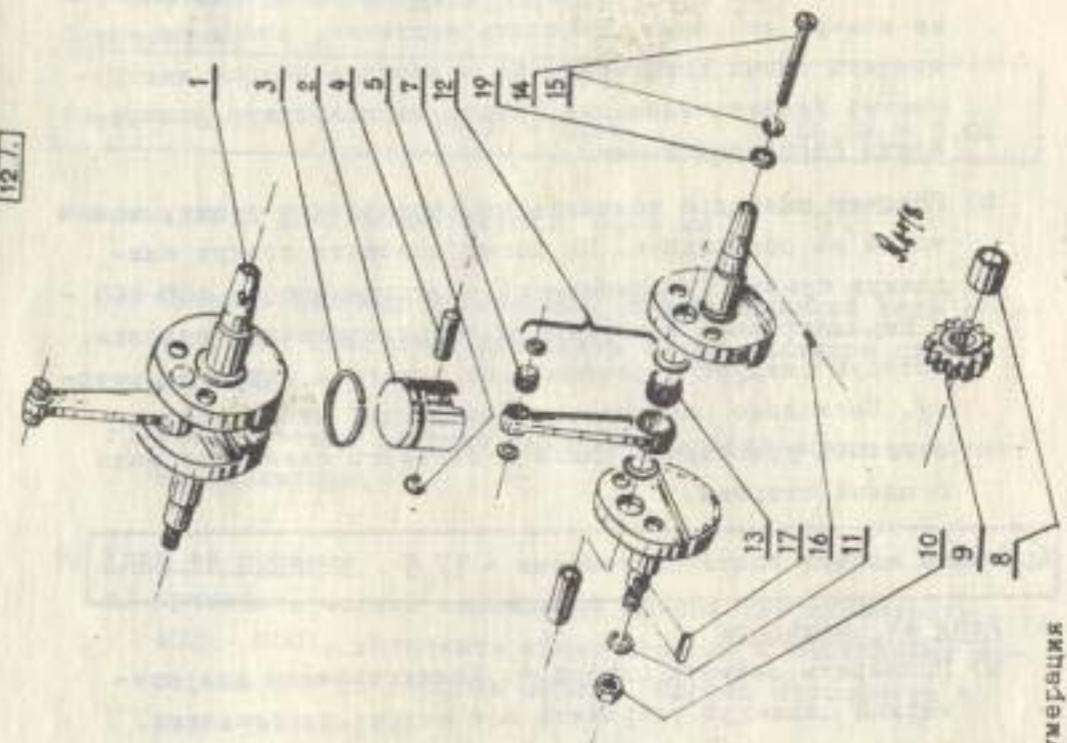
Разложенные части цилиндра и картера двигателя - нумерация в описании деталей.
